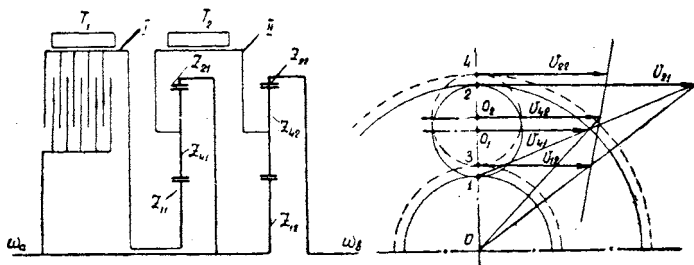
Схема редуктора коробки передач ЗИЛ-111
